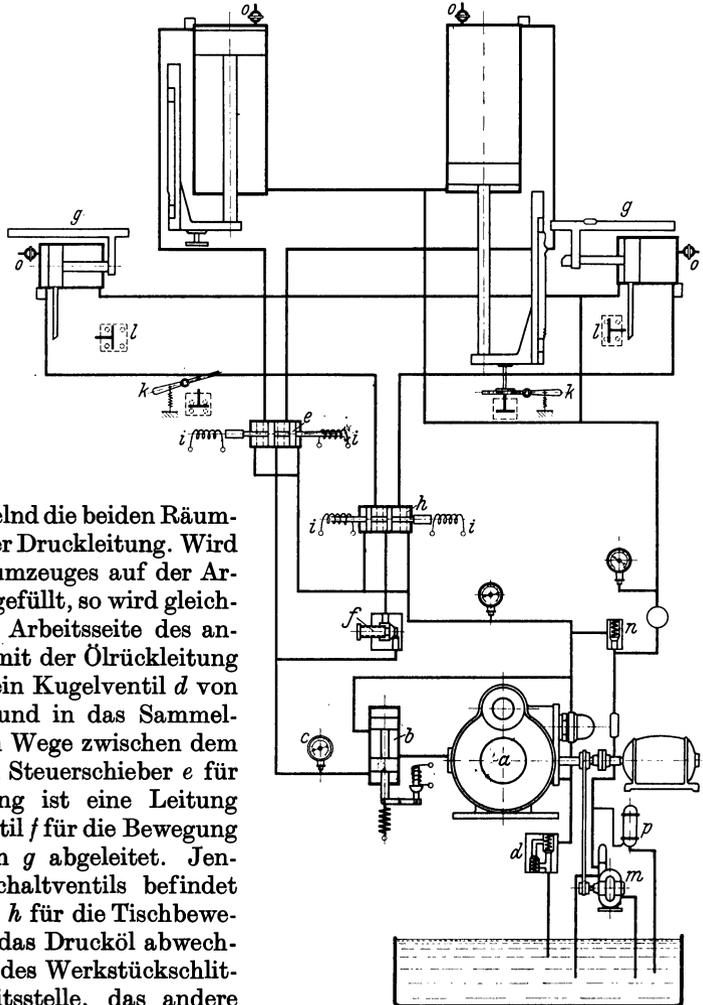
Ölkreislauf einer Zwillingsräummaschine mit Tischbewegung und selbsttätiger Schaltung.
